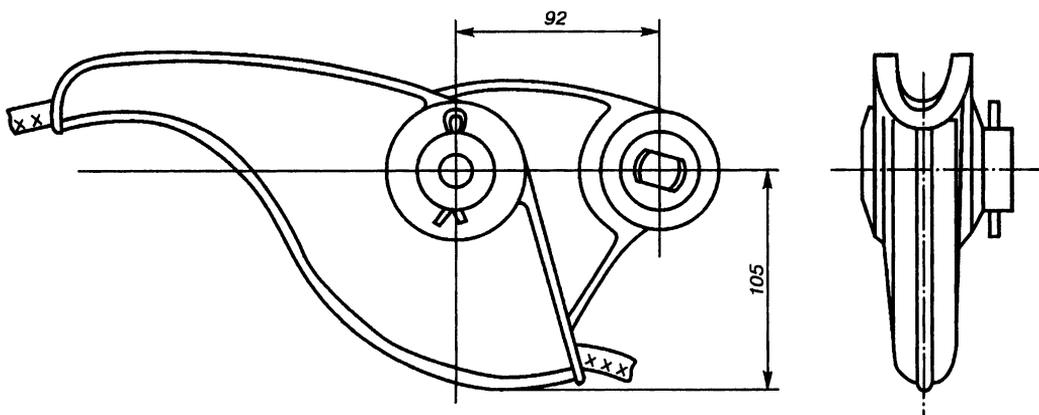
Зажим натяжной заклинивающийся НЗ–2–7
